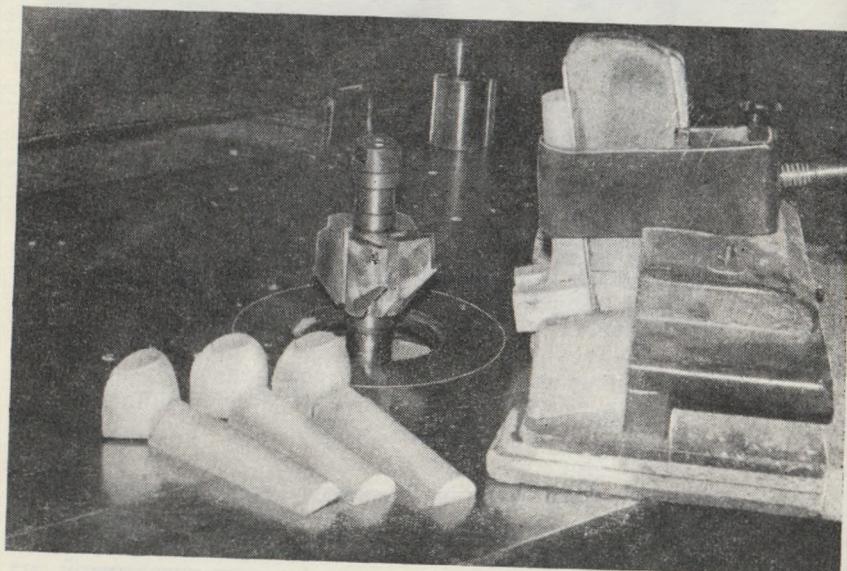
Обработка клеца ручки овальной мандолины на фрезерном станке
